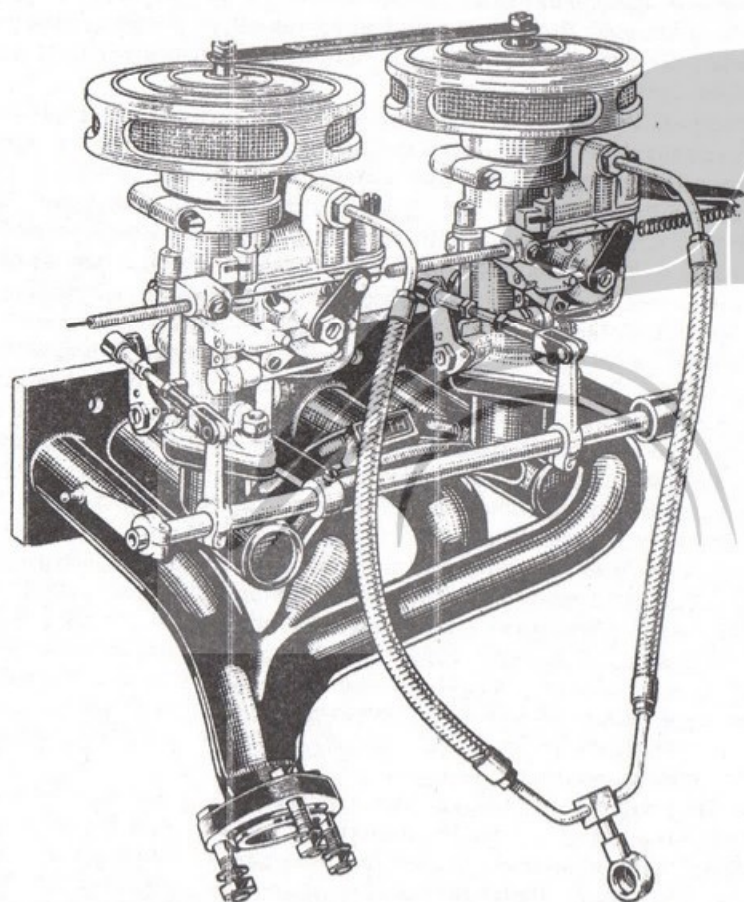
Collettore ABARTH a due carburatori, muniti di depuratori Abarth, per motori della «500» B e C.
